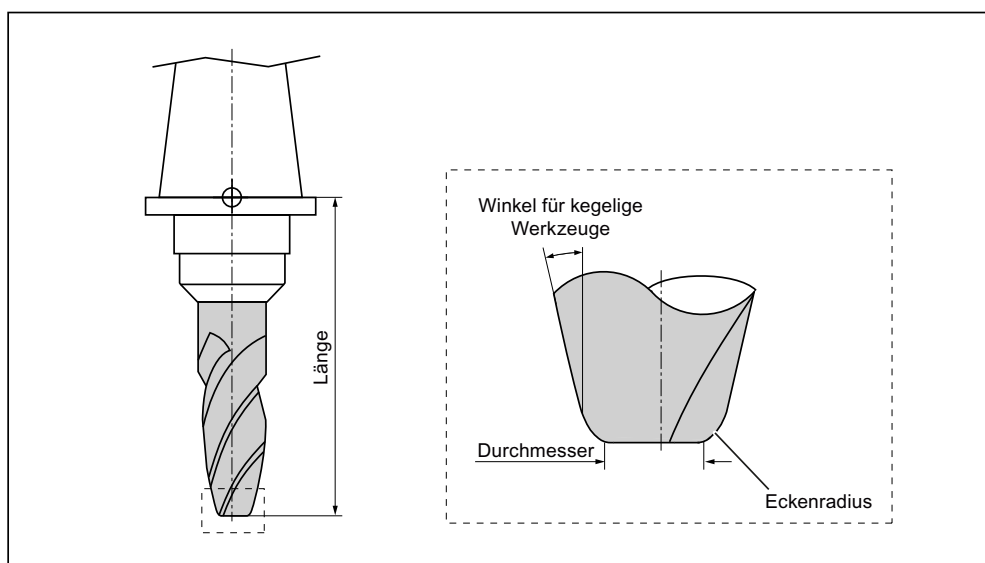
3D-Werkzeug am Beispiel eines Kegelstumpffräasers mit Eckenverrundung (Typ 156)
